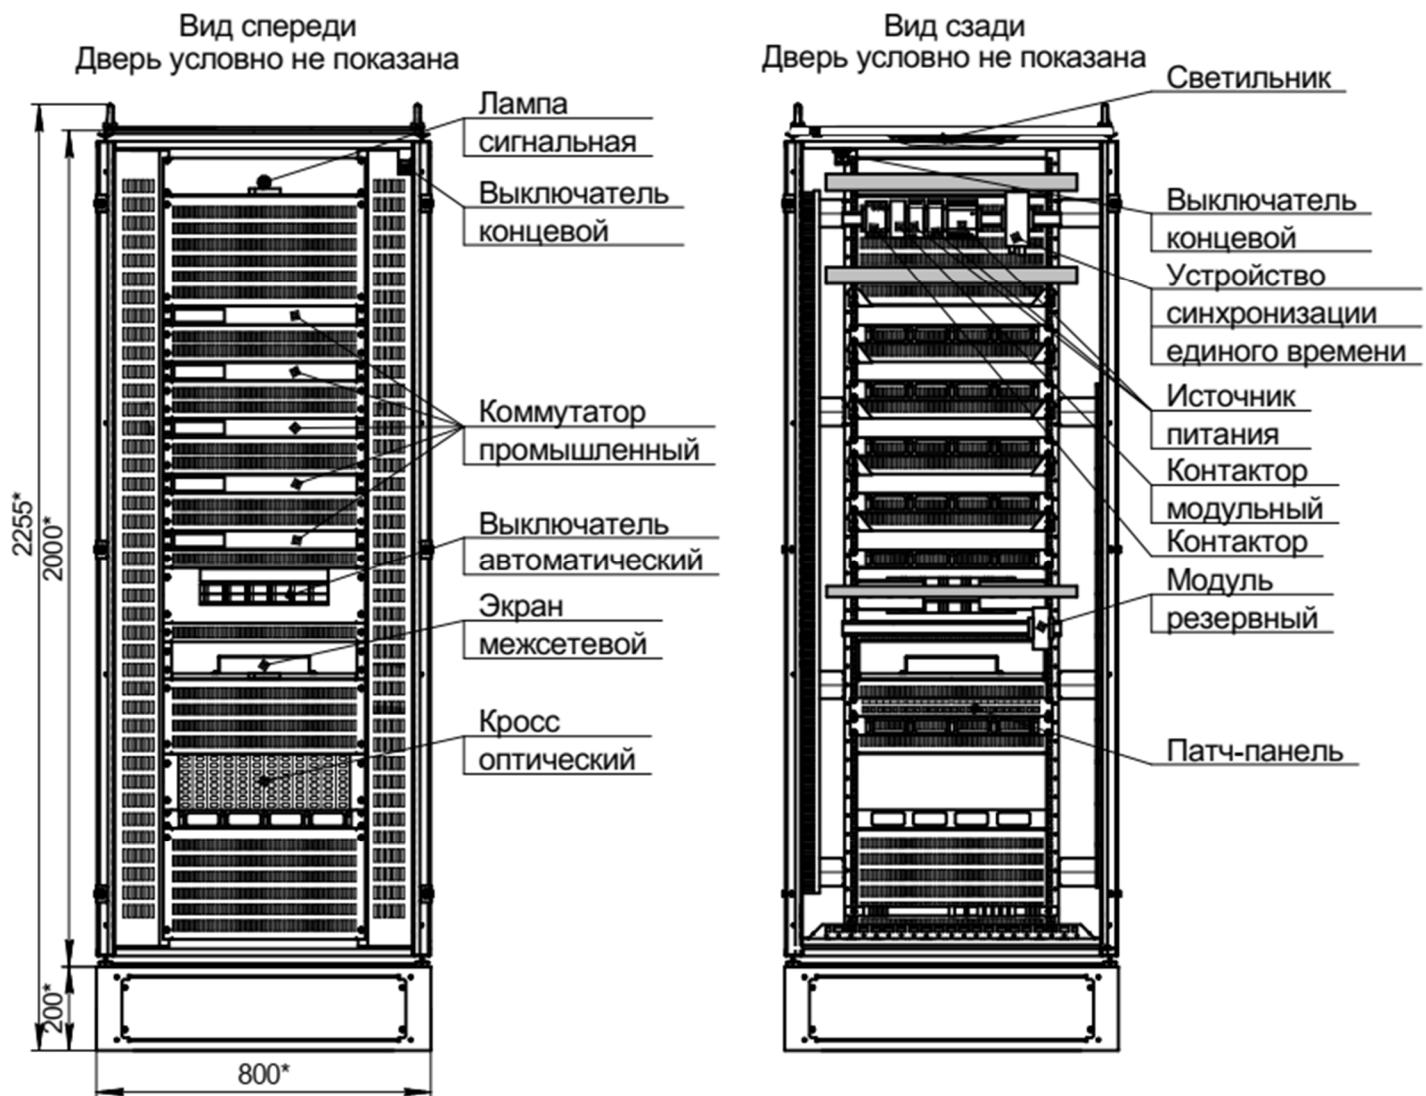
Общий вид и размеры шкафа № ЗНИ
